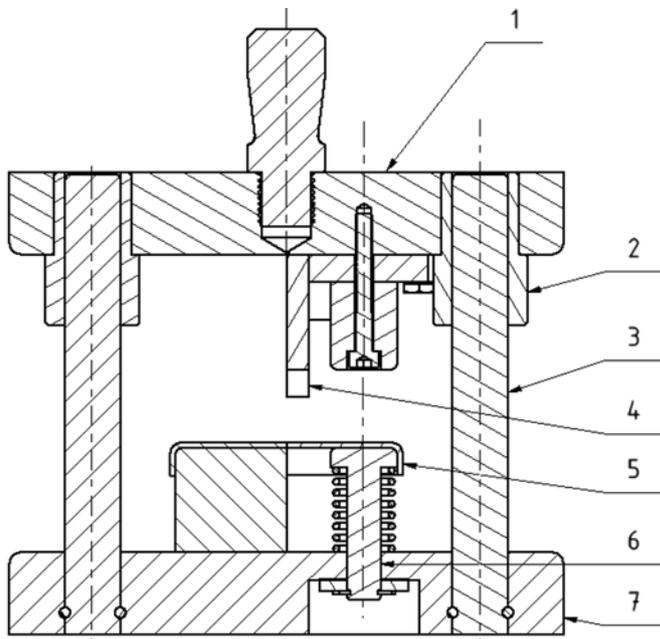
Schneid- und Ziehwerkzeug für Kappe mit Bohrung
